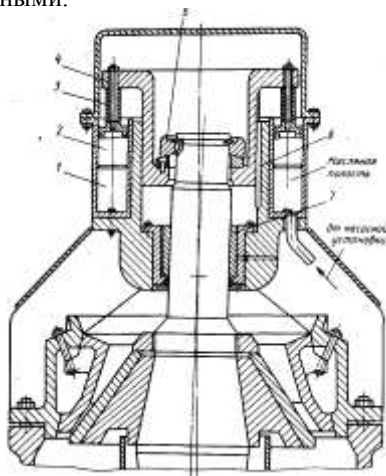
Верхний подвес дробилки фирмы «Кеннеди Ван Саун»: 1 – гидравлический блок; 2 – поршень; 3 – распорная втулка; 4 – подвижный стакан; 5 – сферический подвес; 6 – направляющая шпонка; 7 – конусная втулка.
